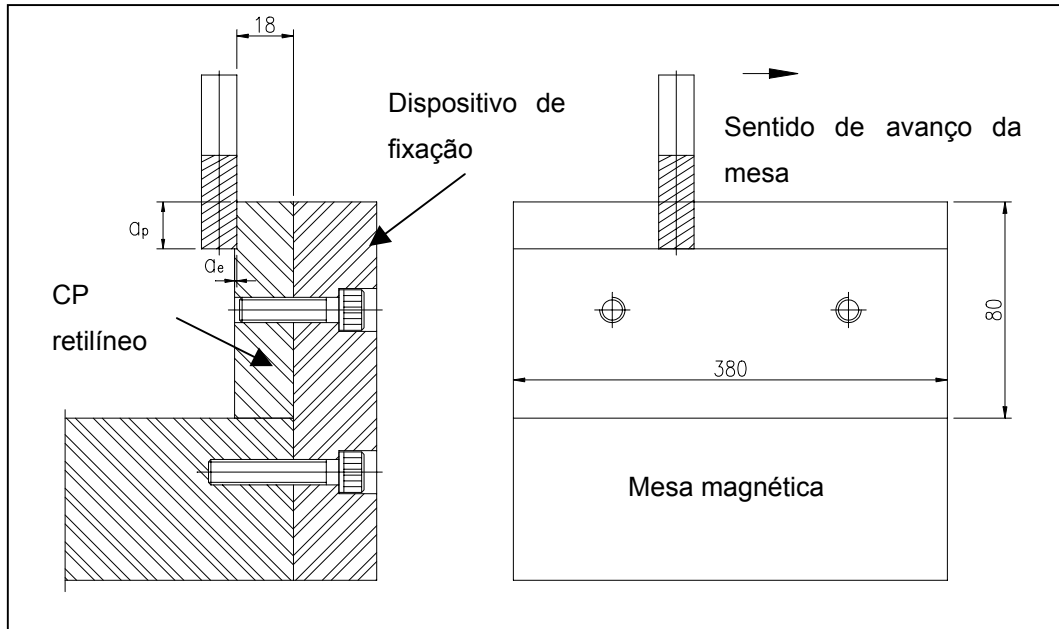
Montagem do CP retilíneo à mesa da máquina-ferramenta.
